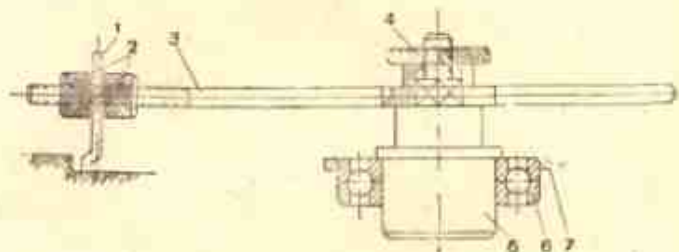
Приспособление для расточки фланца газораспределительной коробки.
